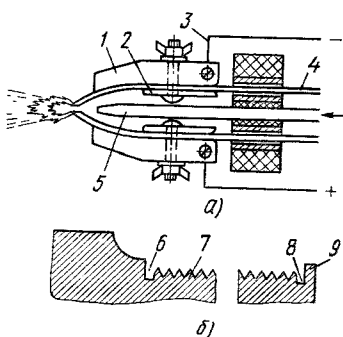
Устройство распылительной головки (а) и подготовка поверхности под напыление (б)
